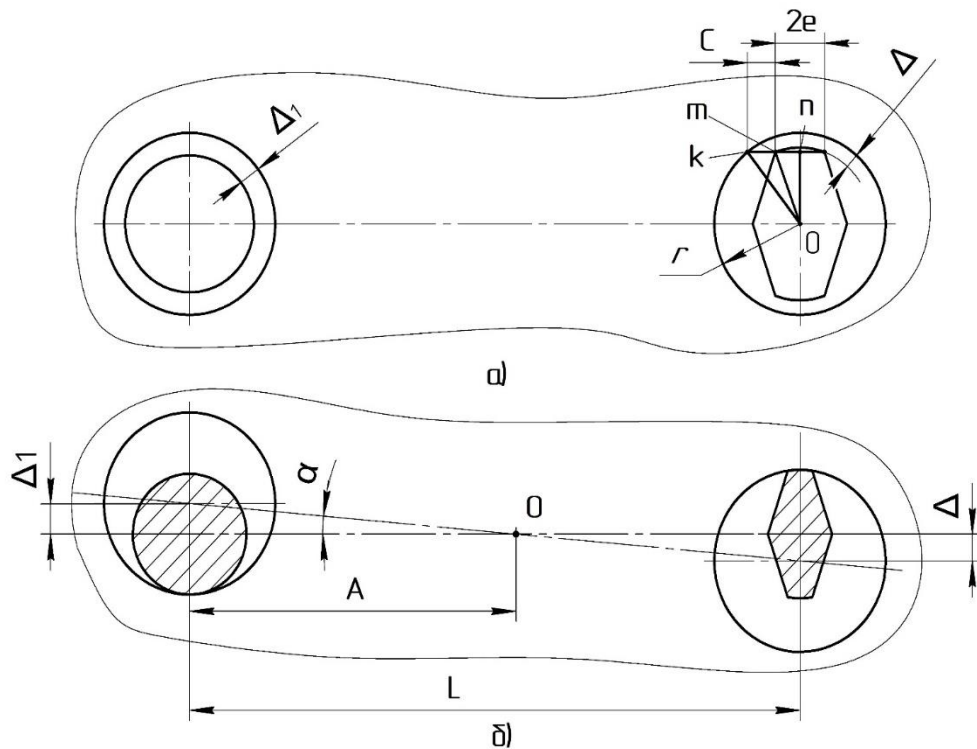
Схема для розрахунку ширини стрічки ромбічного пальця (а) і похибки (б) установаження заготовки на пальці
